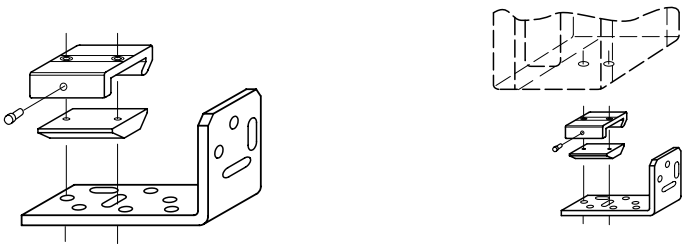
Vue du dispositif à serrage rapide avec équerre
